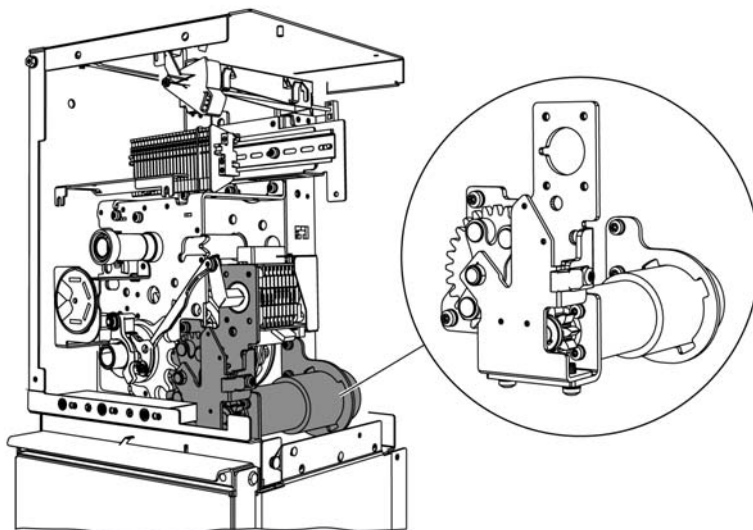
Электродвигательный элемент пружинно-скачкового привода в ячейке кольцевого кабеля
